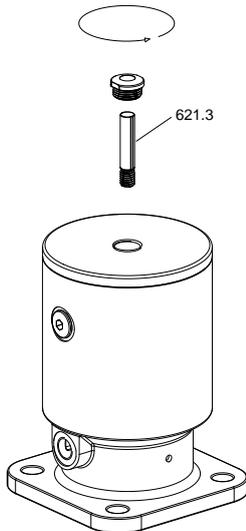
Desmontaje de la caperuza y del indicador de posición LAP.520/.530
